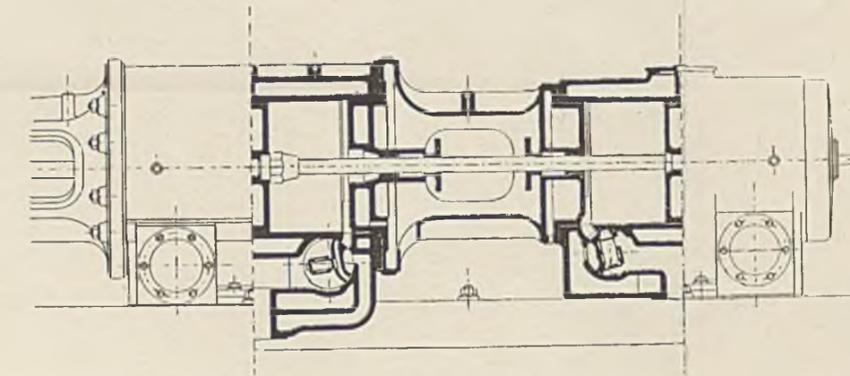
Schnitt durch die Niederdruckeylinder des liegenden Stufen-Kompressors von Th. Calow & Co., Bielefeld.
